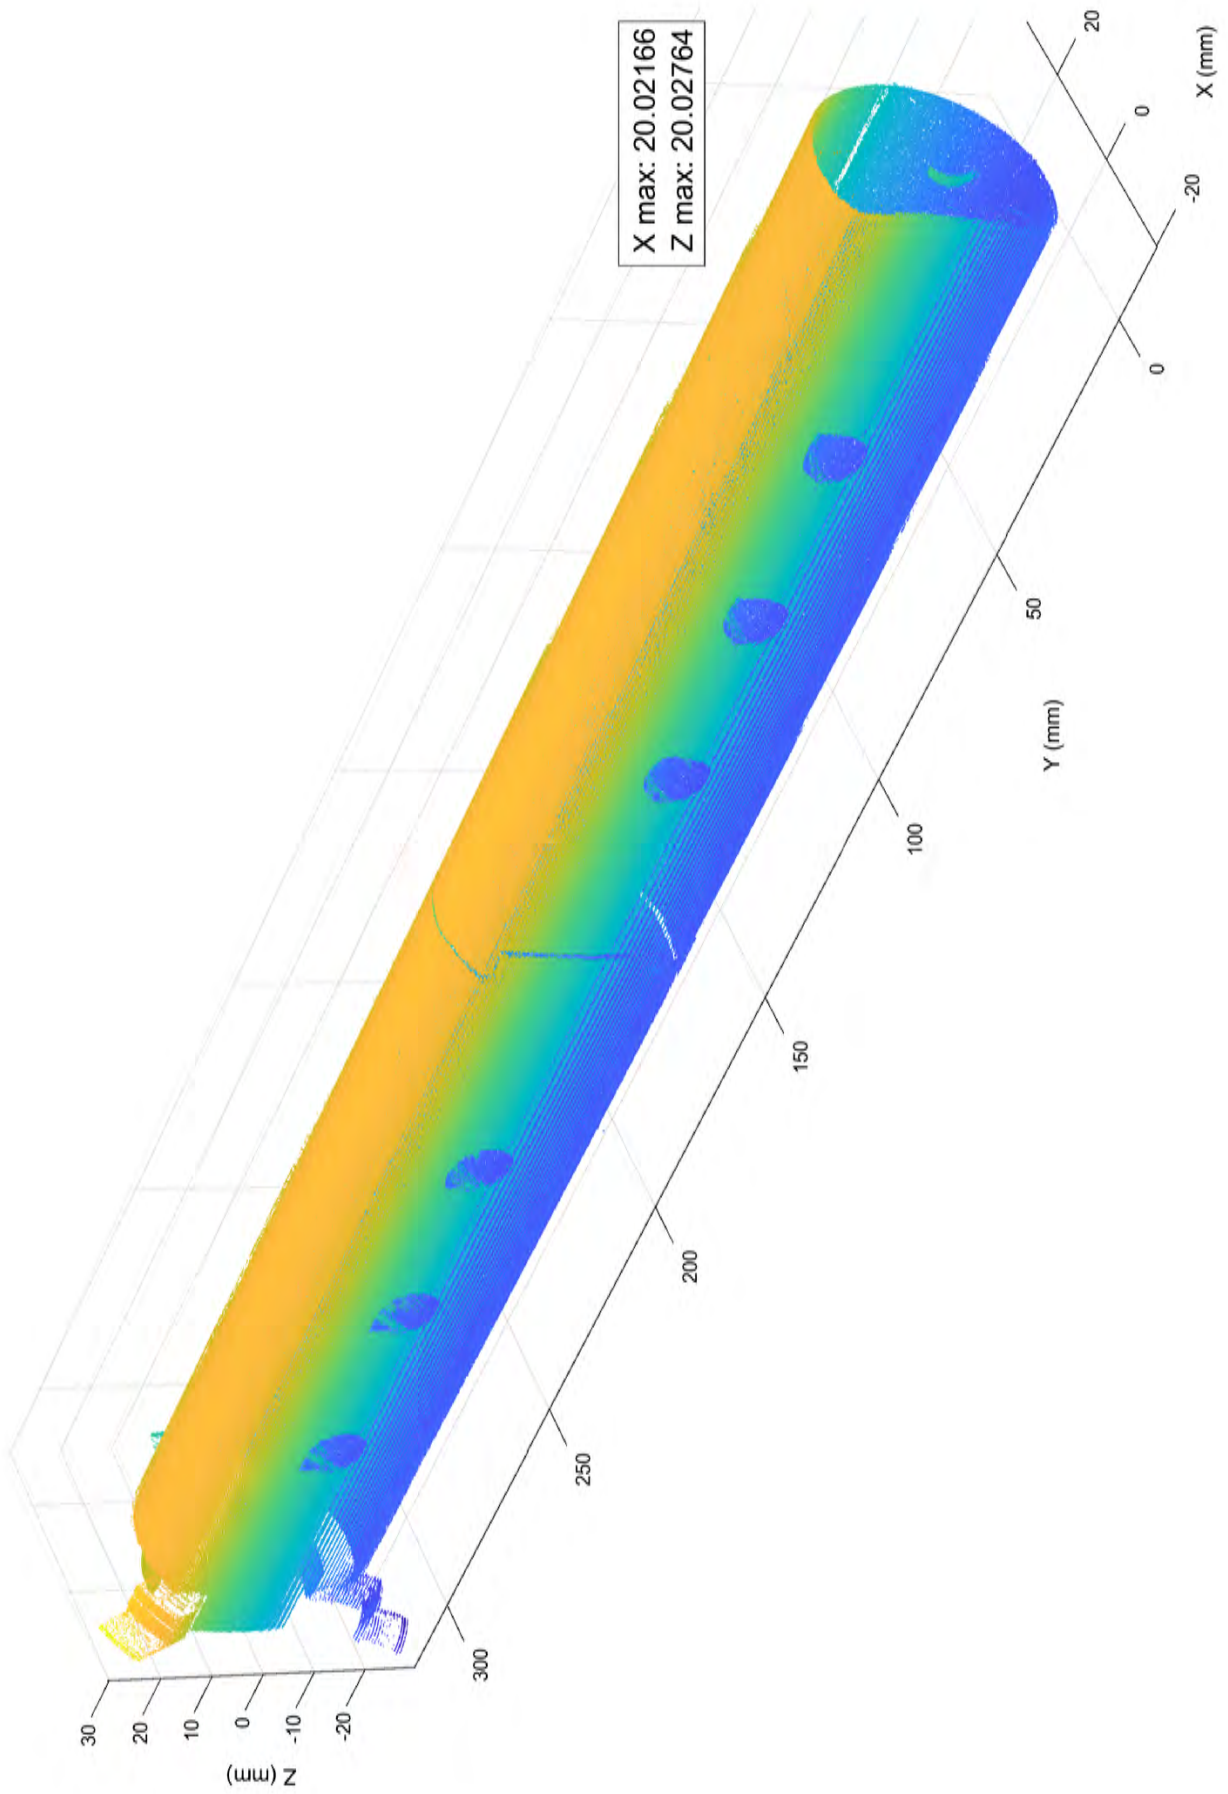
Segunda reconstrucción tridimensional del cilindro de ajuste del plano láser
